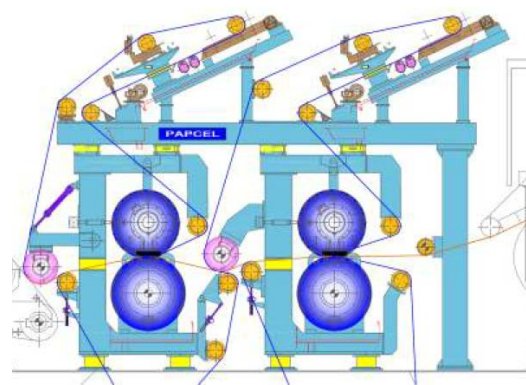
Lisová část papírenského stroje, výrobce Hergen paper machinery (BR) [15]
